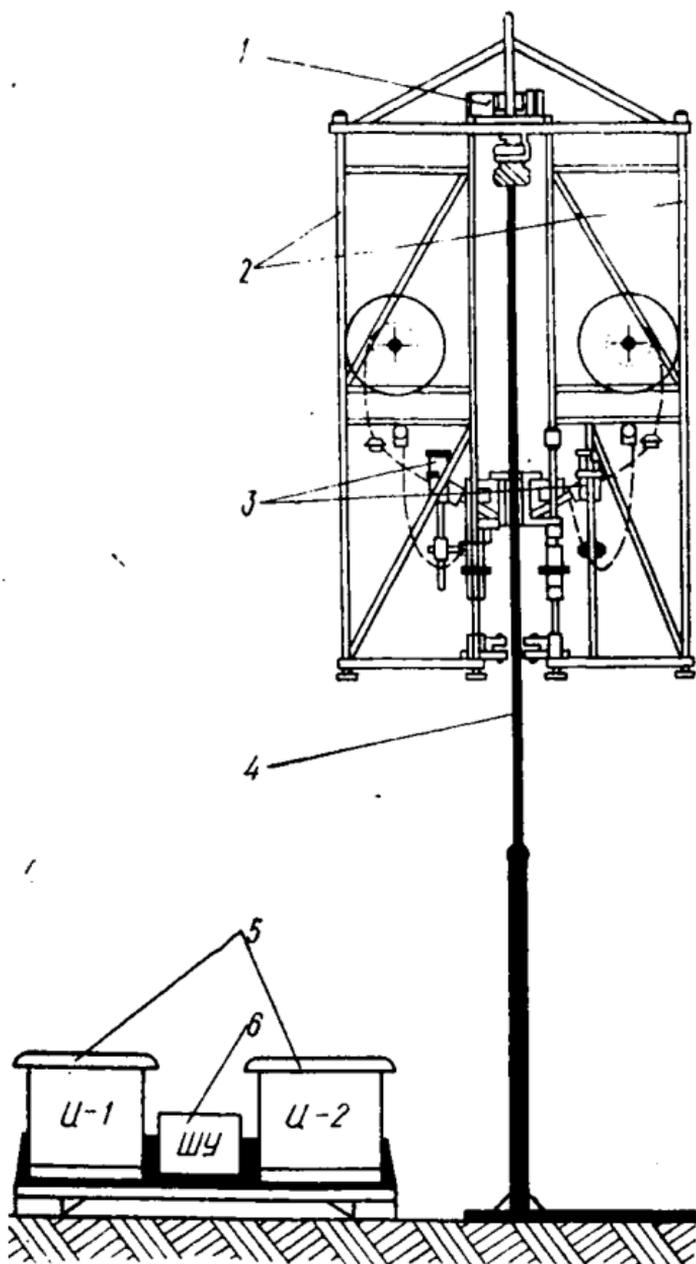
Схема установки «Циркоматик» для сварки горизонтальных швов порошковой проволокой:
